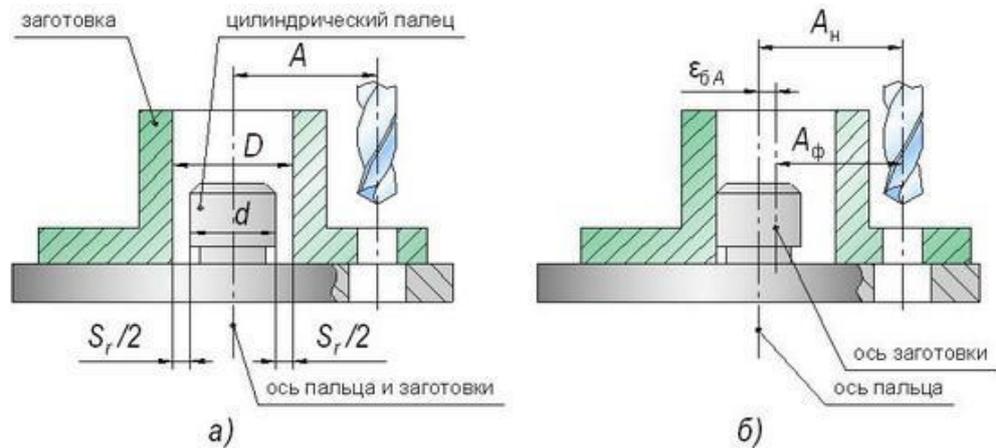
Базирование заготовки на цилиндрическом пальце
